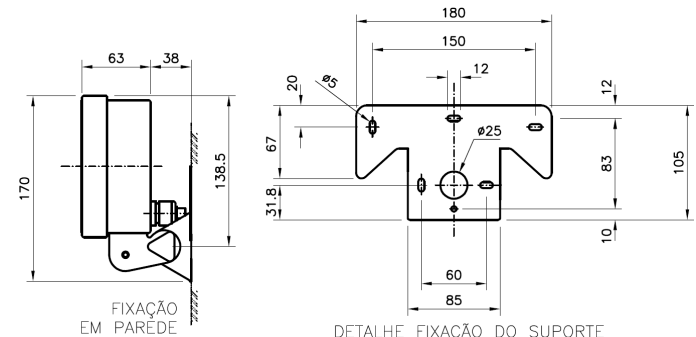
Linha 3100C detalhe fixação em parede e suporte
